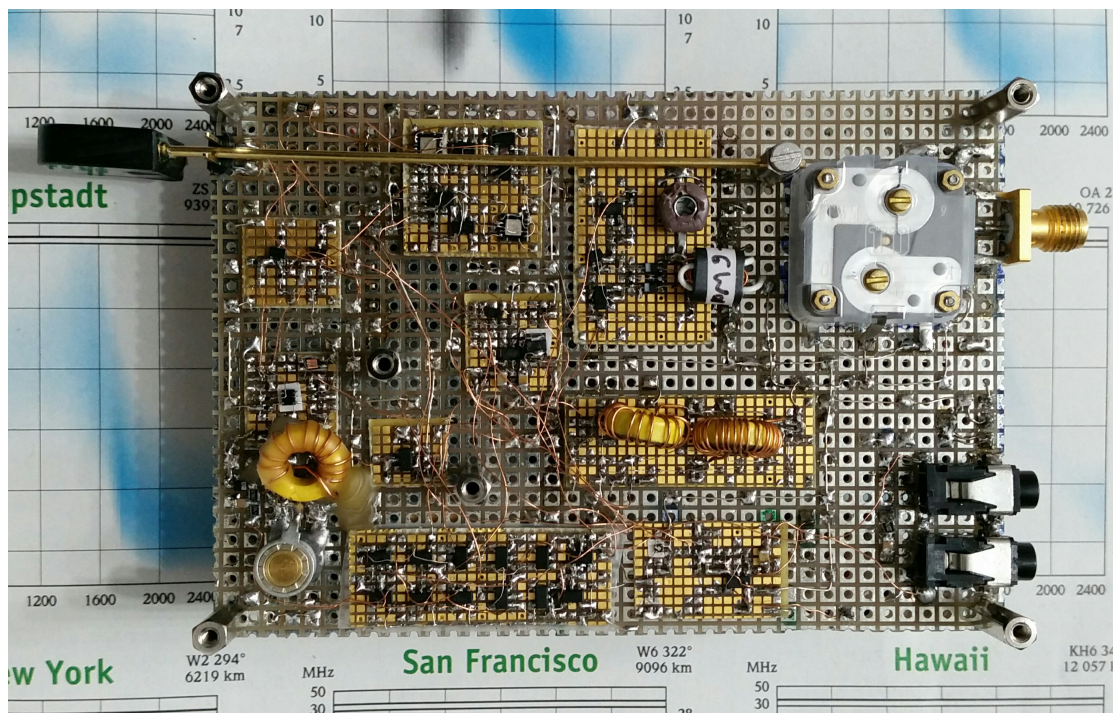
Unterseite mit SMD-Baugruppen auf Adapterplatinen
